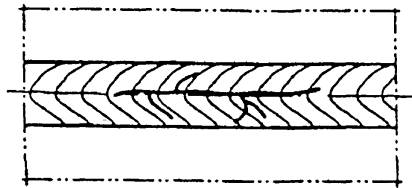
Разветвленная трещина сварного соединения
